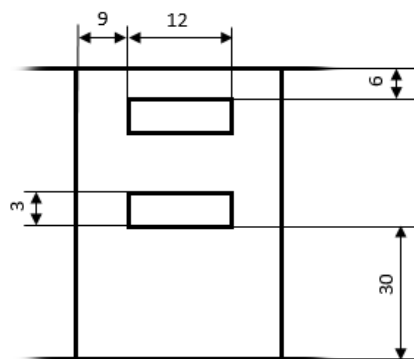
Detalle acotado del lateral de las placas cruzadas
